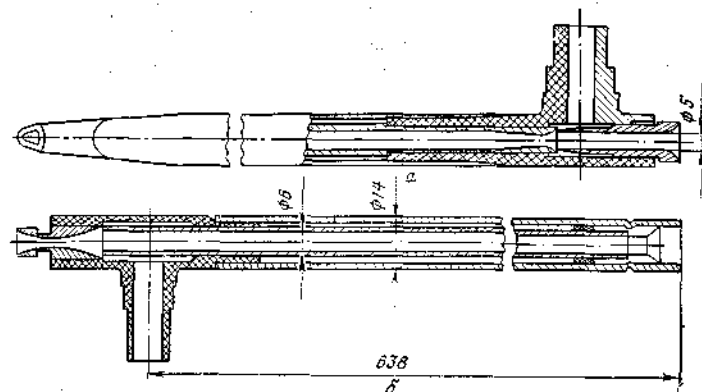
Схема рапиры станка АТПР-120-ЛМ
